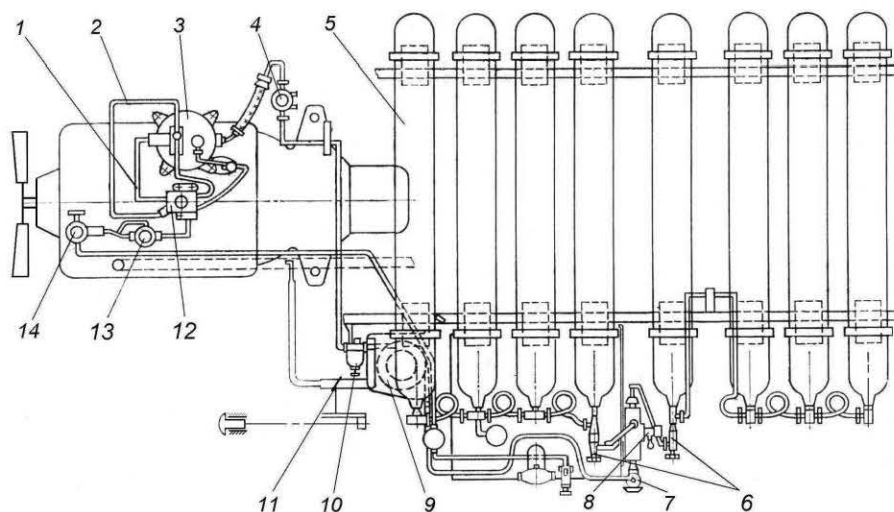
Схема газового обладнання автомобіля ГАЗ-3307: 1 – трубка холостого ходу; 2 – трубка основної подачі газу; 3 – редуктор низького тиску; 4 – електромагнітний клапан газу; 5 – балон; 6 – витратний вентиль; 7 – магістральний вентиль; 8 – заправочний вентиль; 9 – підігрівач; 10 – редуктор високого тиску; 11 – заслінка підігрівача; 12 – карбюратор-змішувач; 13 – бензиновий електромагнітний клапан-фільтр; 14 – бензонасос.
